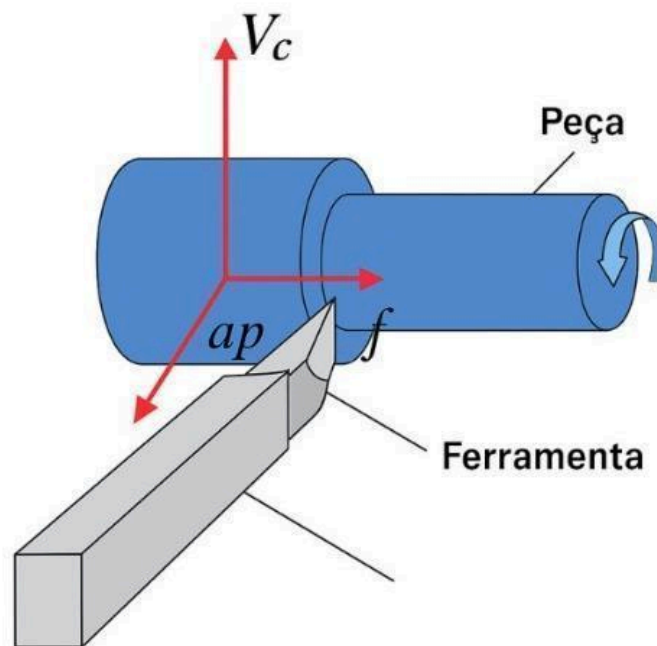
Exemplo esquemático torneamento. Fonte: Autor
